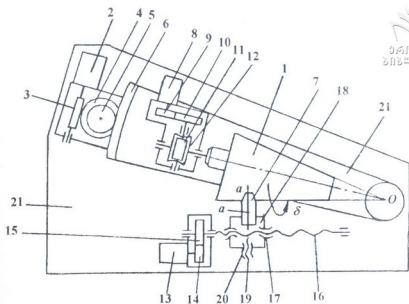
Кинематическая схема станка для нарезания некруглых, круглых конических червяков
